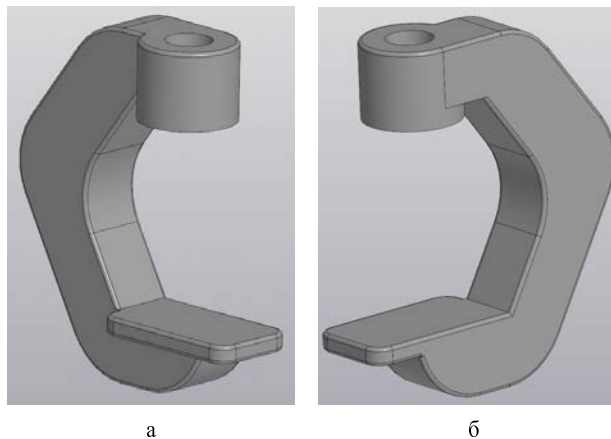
3D модель детали «Кронштейн», а – вид слева, б – вид справа
